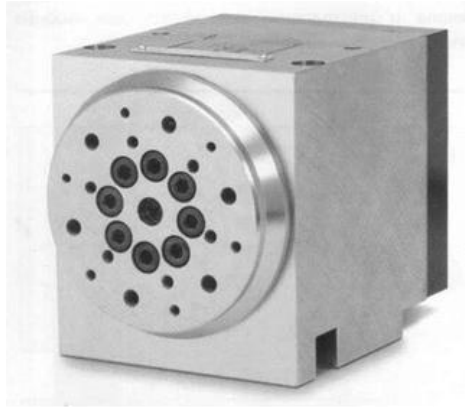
НК.Т110 - одноосьовий поворотний
